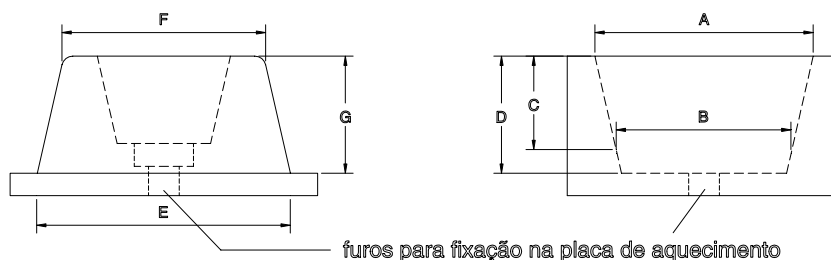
Dimensões dos gabaritos de aquecimento para solda soquete
